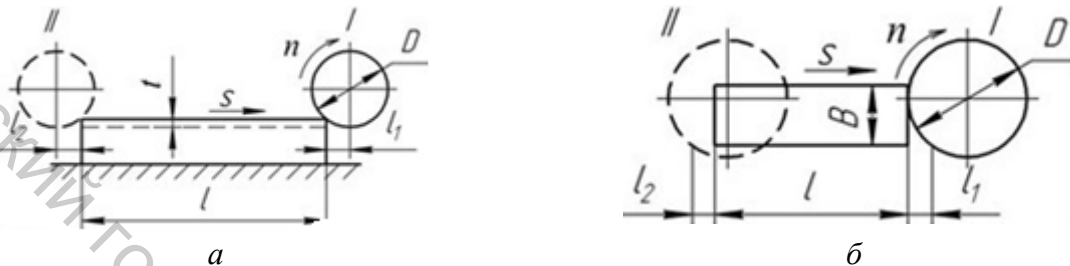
Схемы расчета величины врезания и перебега при фрезеровании: а – концевой фрезой; б – несимметричной торцевой фрезой
